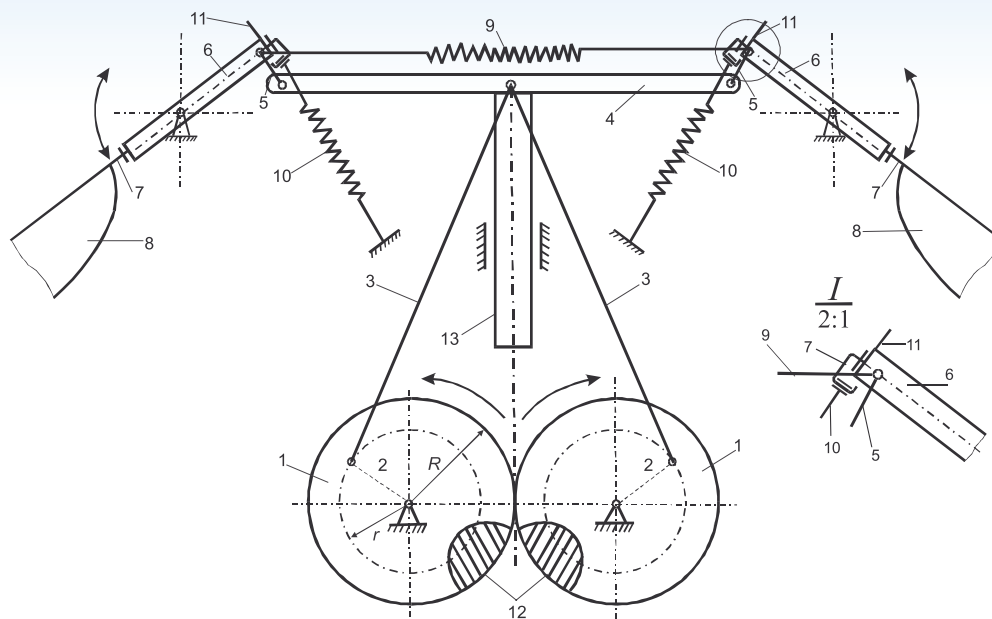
Кинематическая схема механической модели привода быстромашущего движителя – механизма «Автомат супинации»
